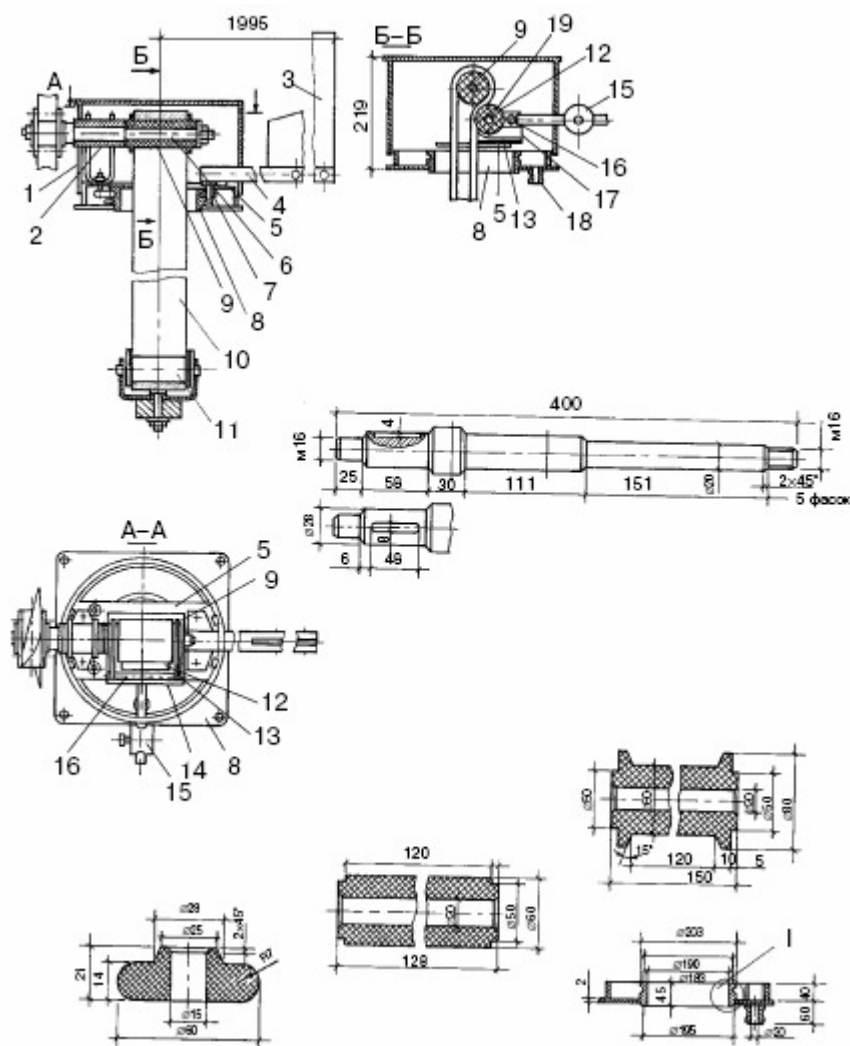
Конструктивная схема водоподъемника: 1 – кожух приводного механизма; 2 – втулка стойки вала; 3 – пластина стабилизатора; 4 – труба стабилизатора; 5 – основание; 6 – вал; 7 – опорный ролик; 8 – корпус приводного механизма; 9 – приводной ролик; 10 – лента-транспортер; 11 – натяжной механизм; 12 – стяжной валик; 13 – рамка основания; 14 – обойма отжимного устройства; 15 – противовес; 16 – ось обоймы отжимного устройства; 17 – водоприемник; 18 – сливной штуцер; 19 – ось стяжного валика
